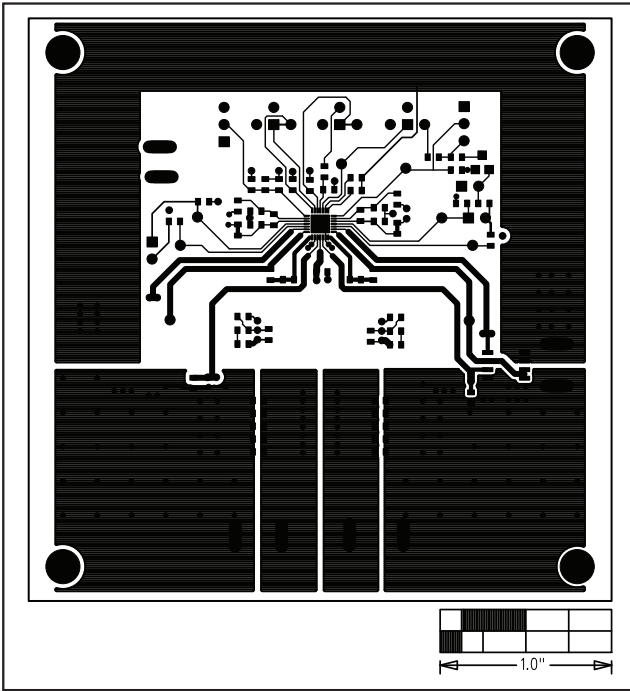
MAX17007A 评估板PCB布局—焊接层
